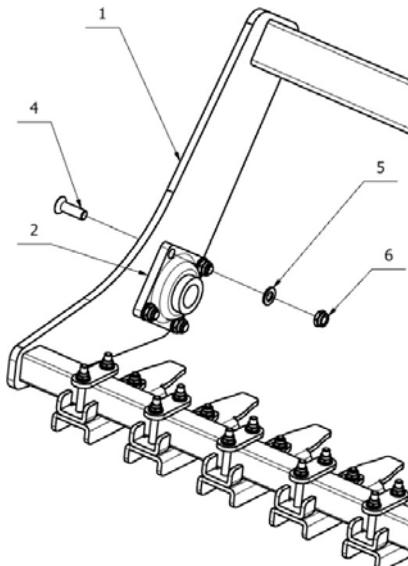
Dachwalze Ø600mm - Lagermontage.
